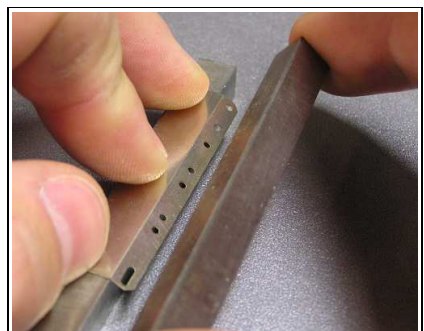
beide Bleche an der eingätzten Linie 90° abkanten. Ätzkante innen!
